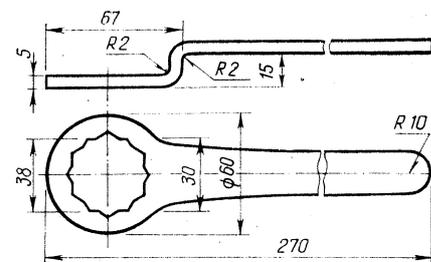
Ключ для поворота коленчатого вала двигателей ВАЗ-2105 и 2107.
